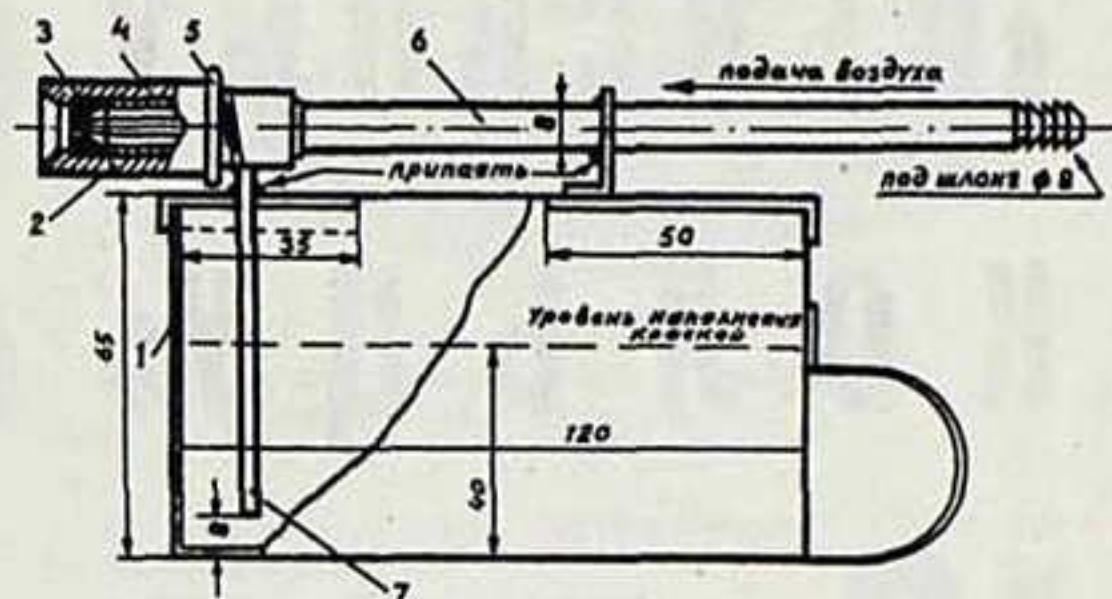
Пульверизатор для окраски: 1 — коробка; 2 — наконечник; 3 — распылитель; 4 — втулка; 5 — контргайка; 6 и 7 — трубки.
